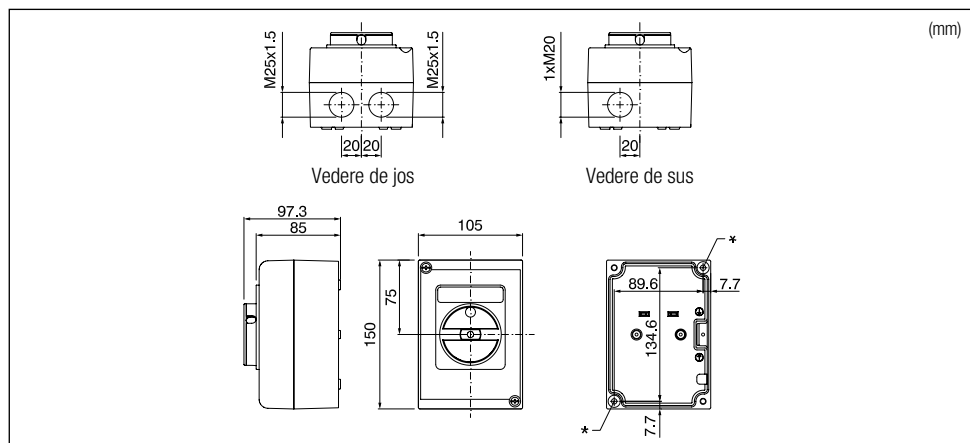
Dimensiuni întrerupător de manevră - separator în casetă 20-32-40A . \* Găuri de fixare pe perete.
